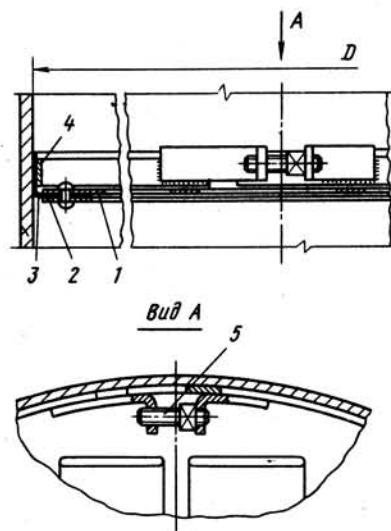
Конструкция нестандартного исполнения решетчатых тарелок: 1 — тарелка; 2 — прижимное кольцо; 3 — фторопластовая пленка; 4 — распорное кольцо; 5 — болт
